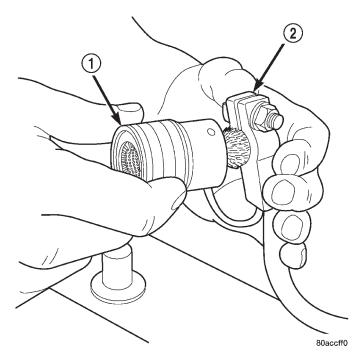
Limpieza de abrazaderas de terminales de cables de la batería - Característica
